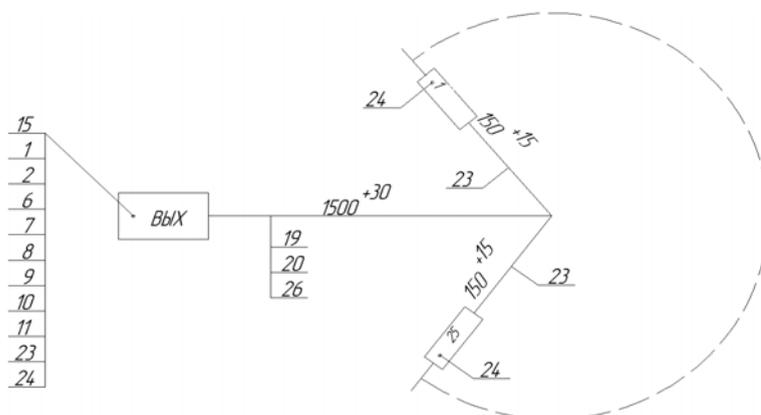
Фрагмент сборочного чертежа жгута со свободными концами
